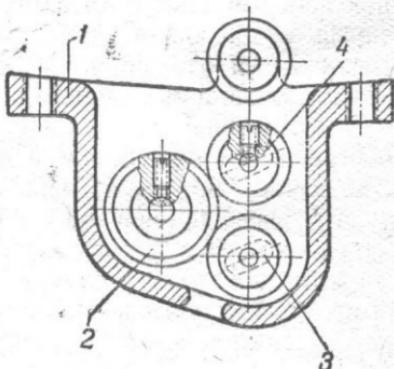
Противопожарный канал в разрезе: 1 — корпус; 2 — ролик; 3 — ролик; 4 — ось
